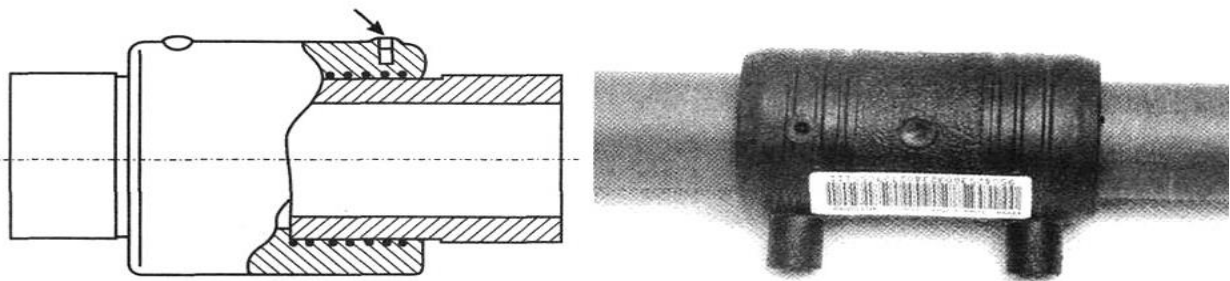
Некачественно выполненное сварное соединение с ЗН (индикаторы сварки в исходном положении)
